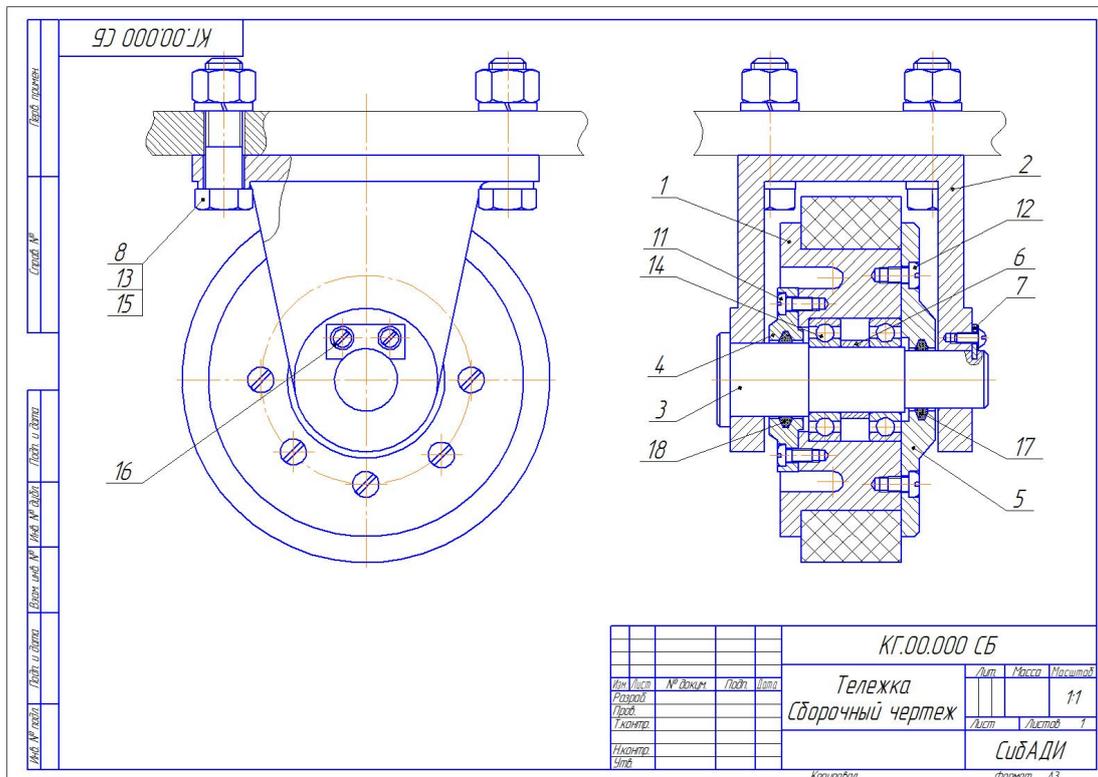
Заготовка сборочного чертежа «Тележка»
